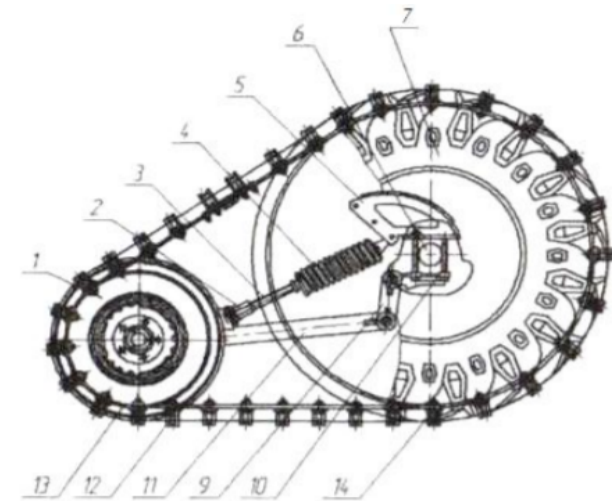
Полугусеничный движитель с резинометаллической гусеницей и штампованными почвозацепами
